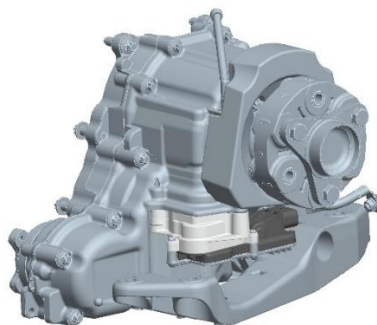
TCU pentru cutie de transmisie AWD (all-wheel drive) [23]
